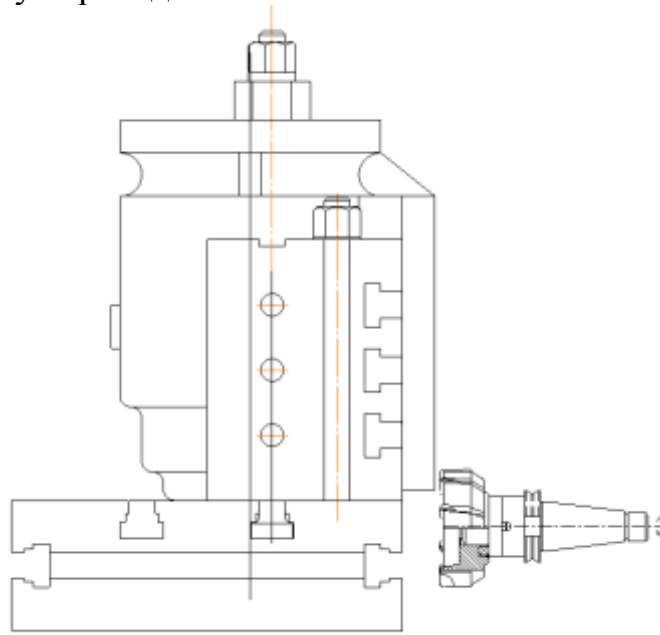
Схема оброблення на переході 01 операції 005. Для розрахунку сили закріплення при торцевому фрезеруванні необхідно нанести сили, які діють на заготовку під час оброблення. На заготовку діють сила різання P , яку розкладаємо по трьом осям на P_X , P_Y , P_Z
